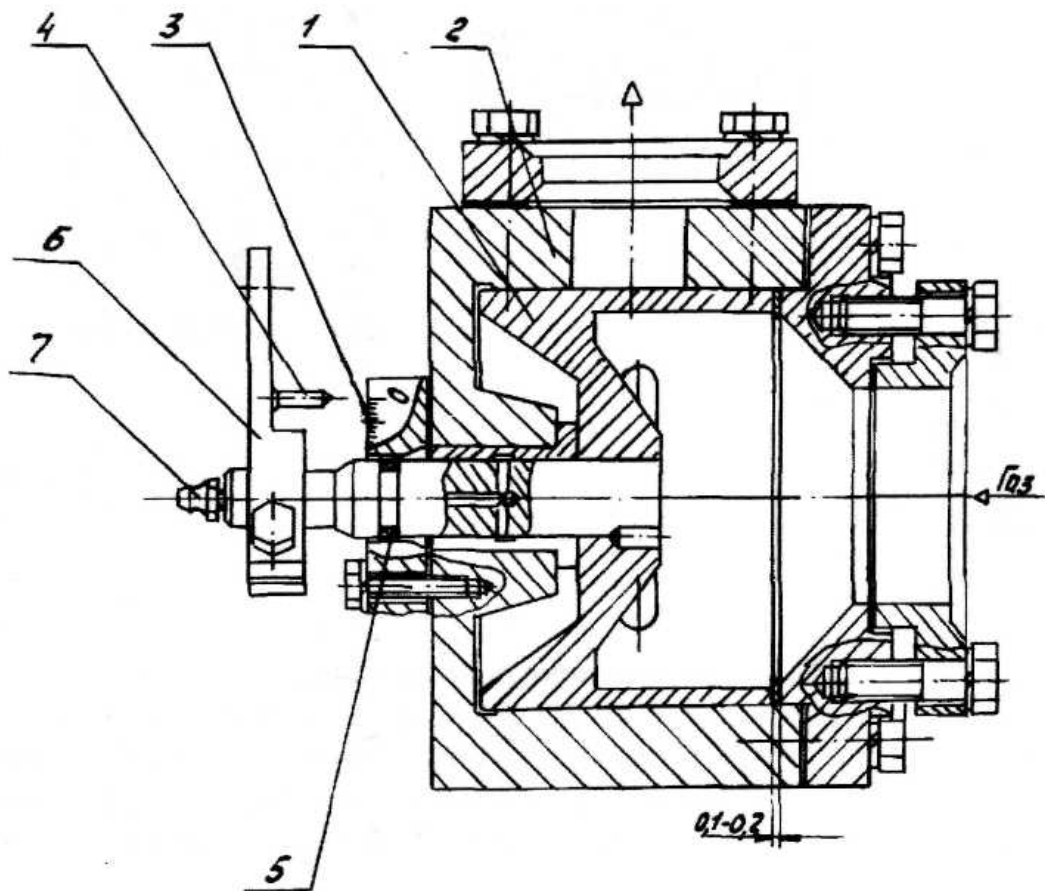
Дозатор газу: 1 – ротор; 2 – корпус; 3 – шкала; 4 – вказчик;
